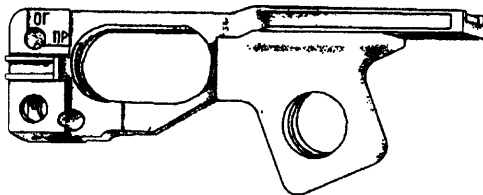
Корпус ударно-спускового механизма с рукояткой
